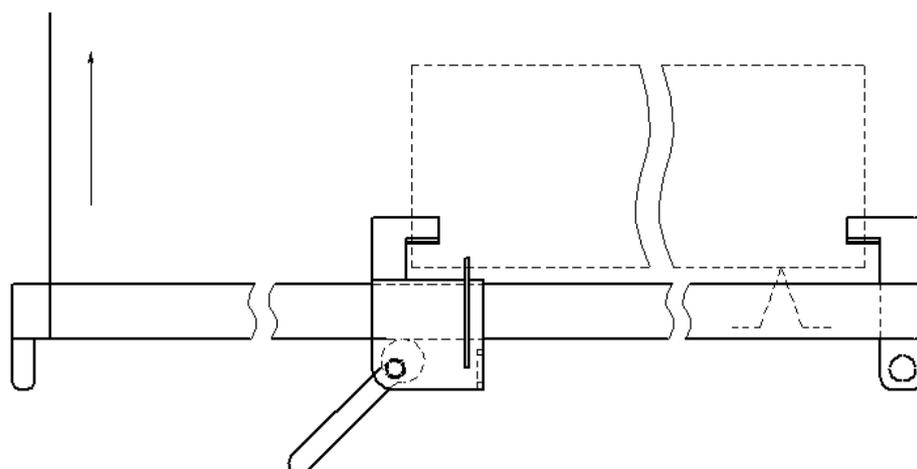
Подъем переднего края бочки для установки раздающего устройства
